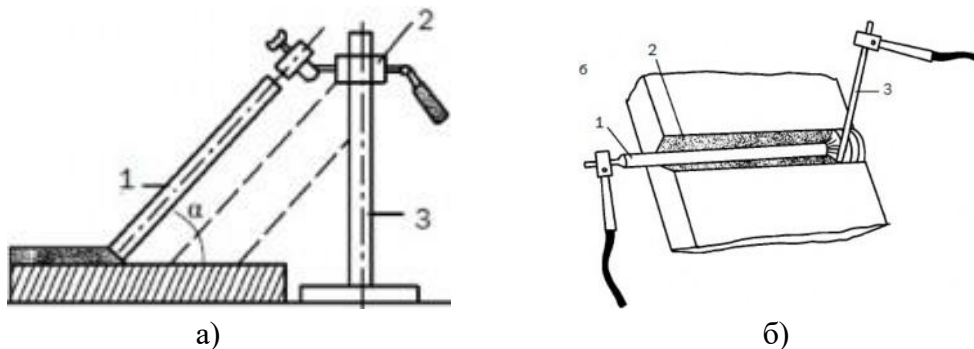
Способы сварки: а - наклонным электродом: 1 - электрод; 2 - обойма; 3 - штанга;
